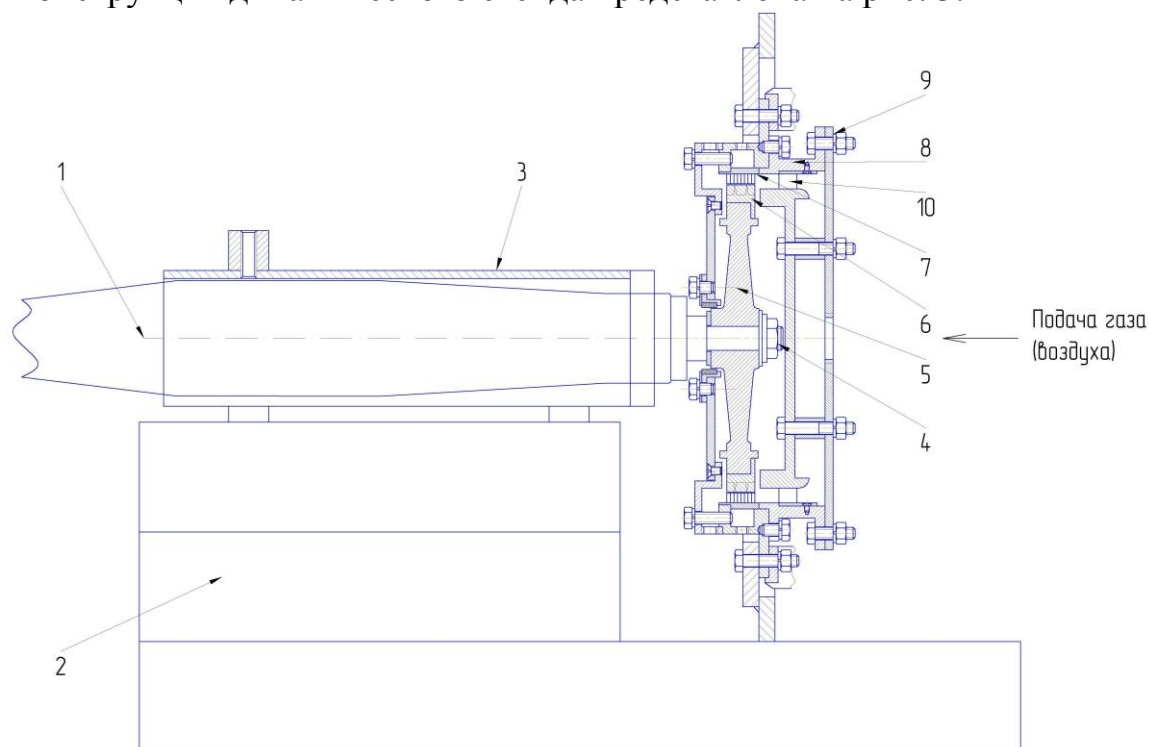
Поперечное сечение динамического стенда: 1 – привод; 2 – станина; 3 – корпус привода; 4 – фиксирующая гайка; 5 – диск; 6 – роторная часть уплотнения; 7 – статорная часть уплотнения; 8 – передний фланец; 9 – задний фланец; 10 – направляющий аппарат
